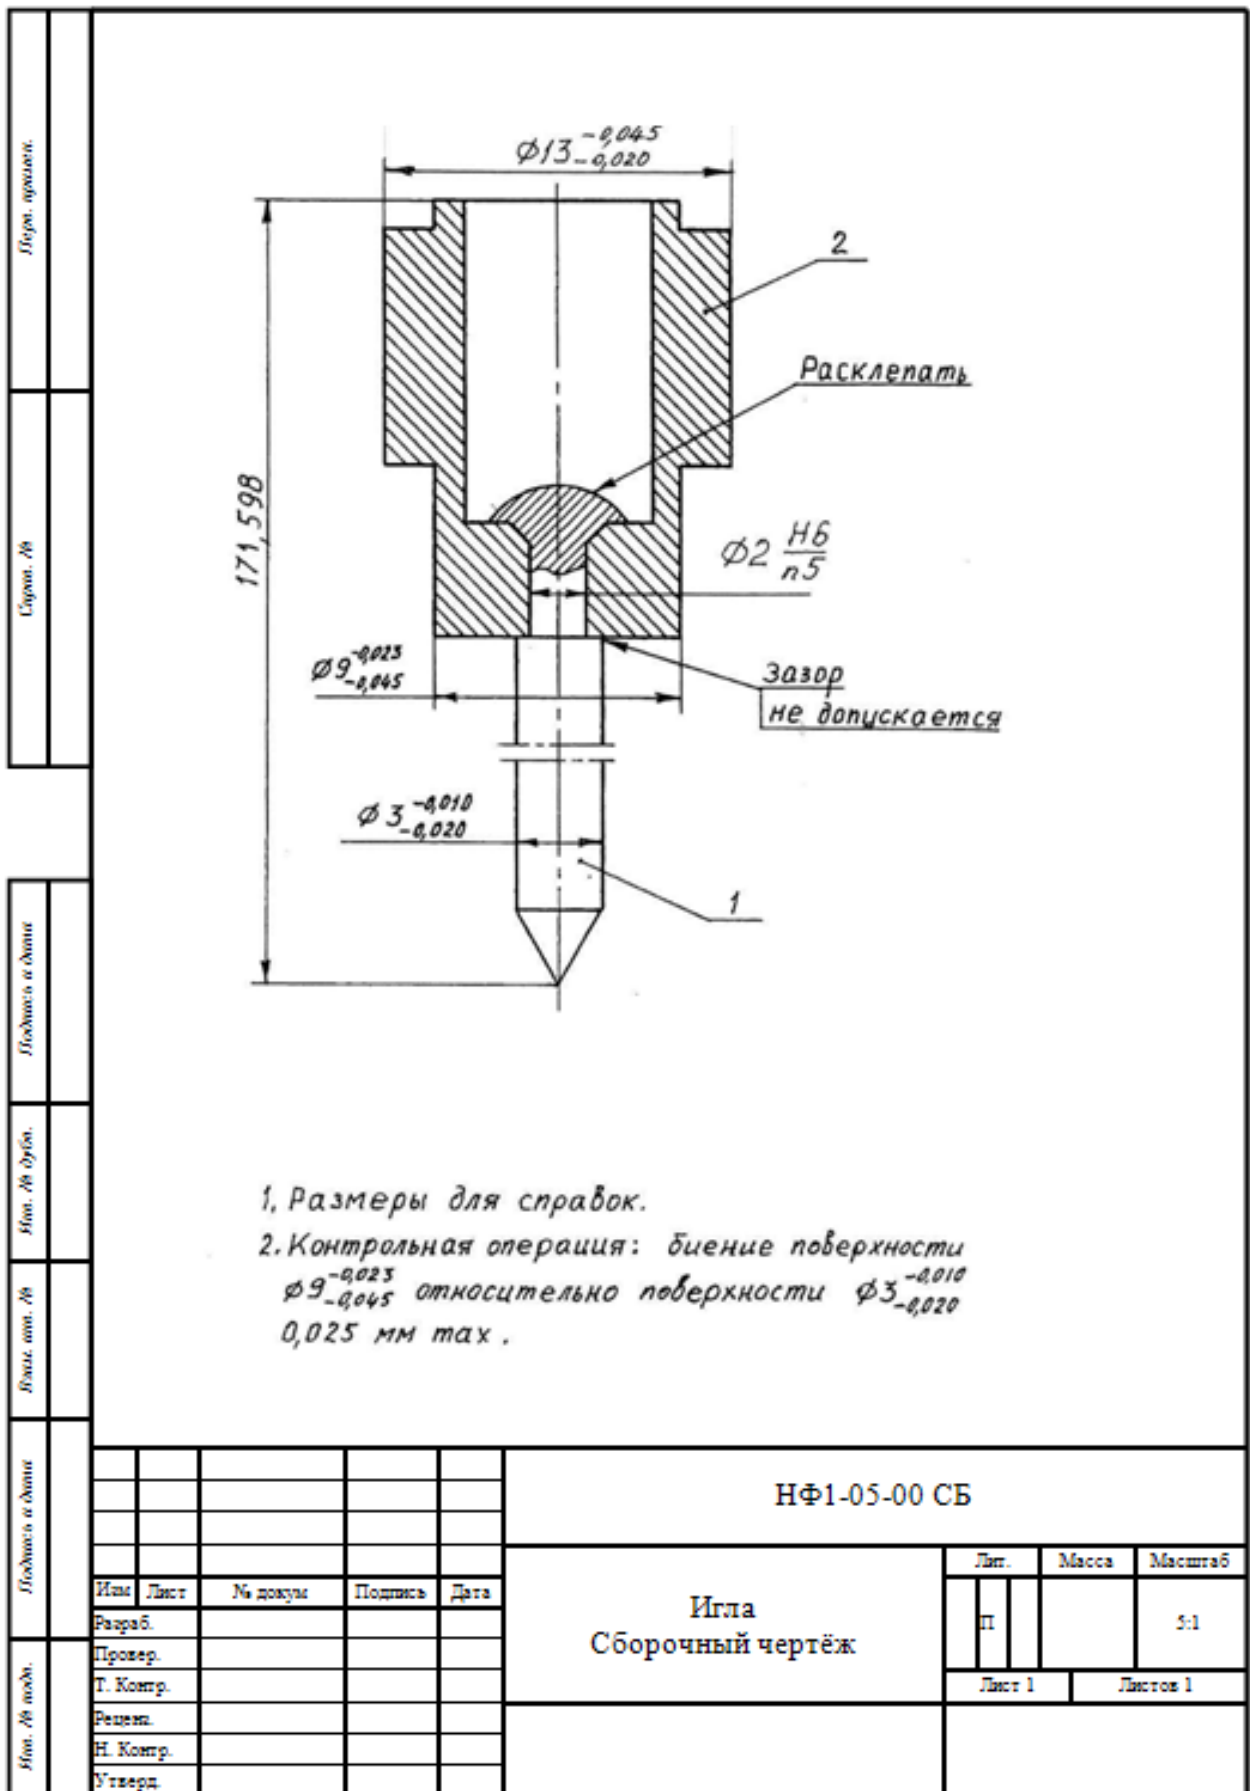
Пример выполнения сборочного чертежа «Игла»
